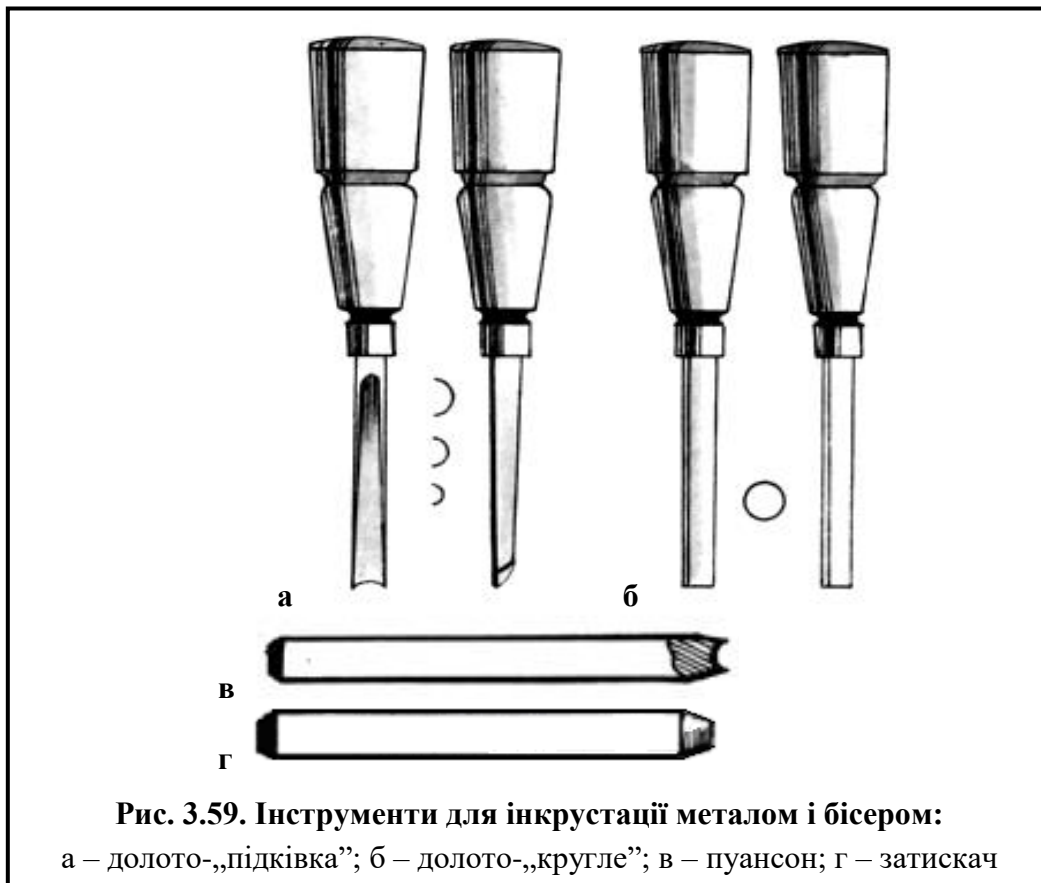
Інструменти для інкрустації металом і бісером:
